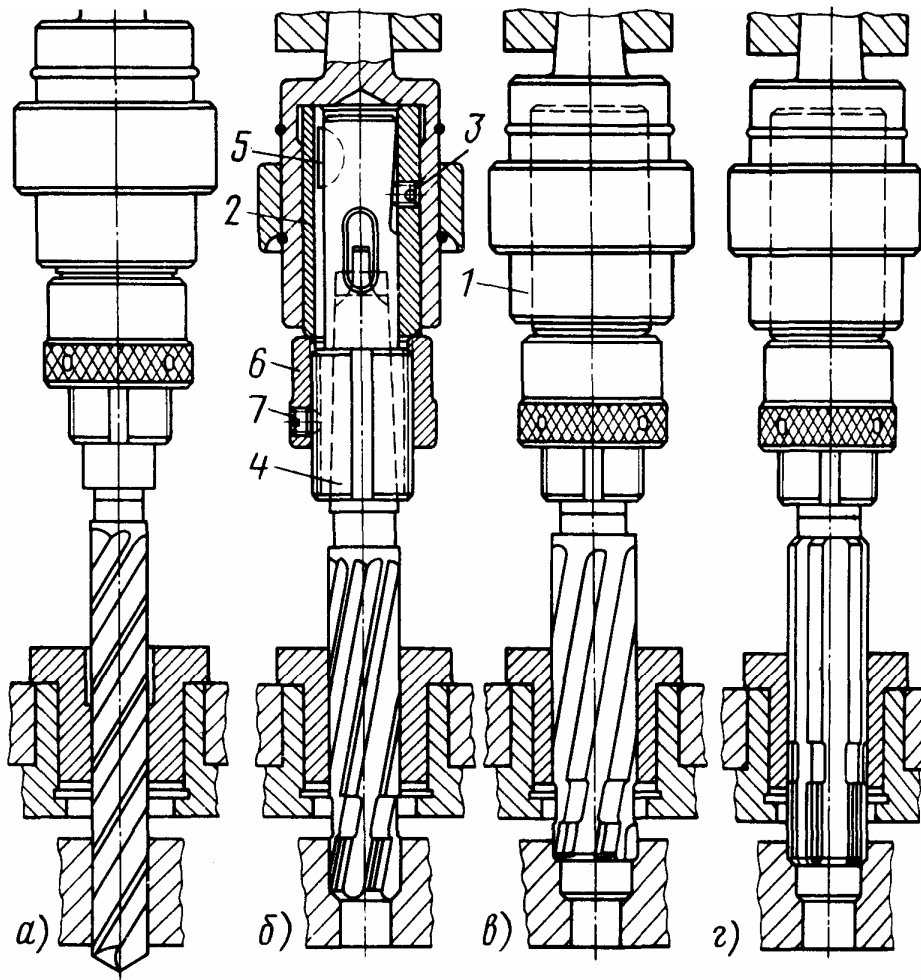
Схеми послідовної багатоперехідної обробки отвору на одношпиндельному свердильному верстаті: 1 – швидкозмінний патрон; 2 – проміжна втулка; 3 – гвинт; 4 – регульована втулка; 5 – сегментна шпонка; 6 – гайка; 7 – гвинт
